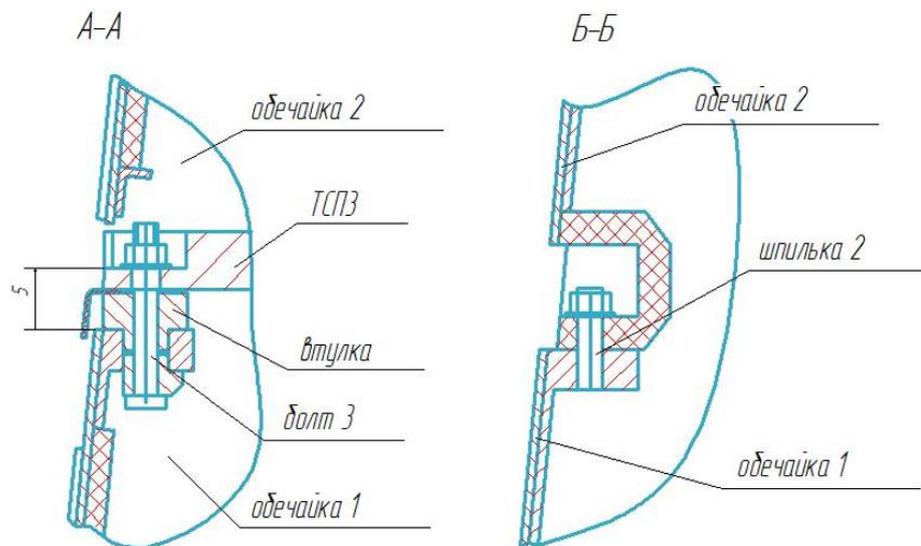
Конструкция стыка обечаек 1 и 2 корпусу МКА
